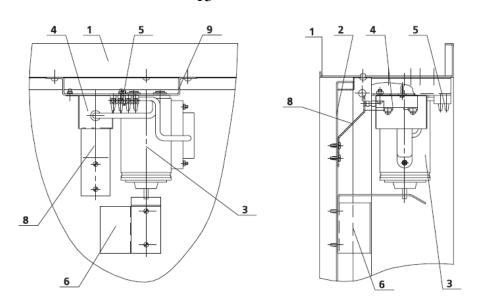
Исполнительный механизм клапана дымоудаления КПД-4-01 и КПД-4-02 производства ООО «Веза» с электромагнитным приводом, установленным внутри: 1 — корпус; 2 — лопатка; 3 — электромагнит; 4 — конечный выключатель; 5 — клеммная колодка; 6 — рукоятка; 8 — прижим конечного выключателя; 9 — монтажная планка исполнительного механизма
